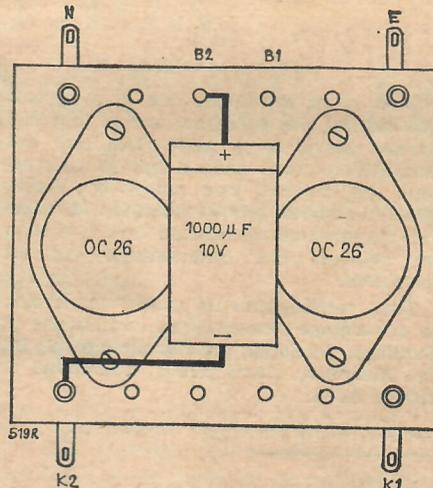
Plaquette du multivibrateur vue de dessus.
